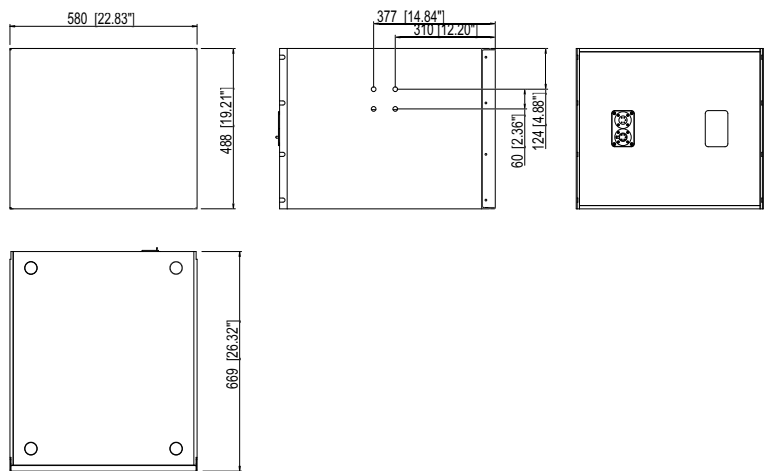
Qi-SUB dimensions du coffre en mm [inch]
